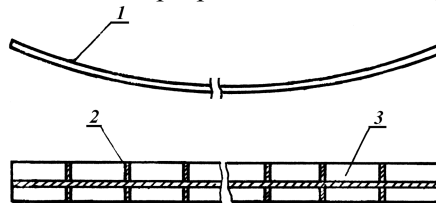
Схема розрізання ресорного листа: 1 – лист, 2 – місце розрізання, 3 – заготовки для виготовлення зразків
